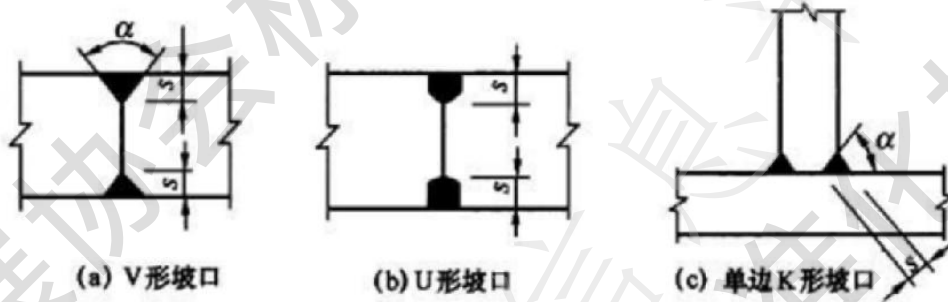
部分熔透的对接焊缝和 T 形对接与角接组合焊缝截面
